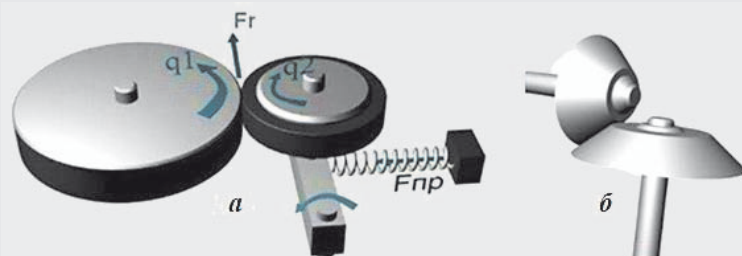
Фрикційна передача: а — з паралельними валами; б — з пересічними валами
